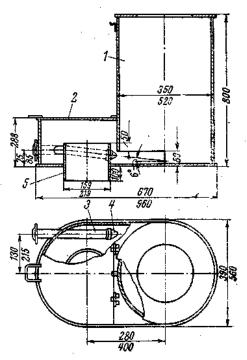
Золосмывной аппарат с гидрозатвором: *I* – корпус; *2* – крышка; *3* – смывной патрубок; *4* – сопло; *5* – сливная труба
